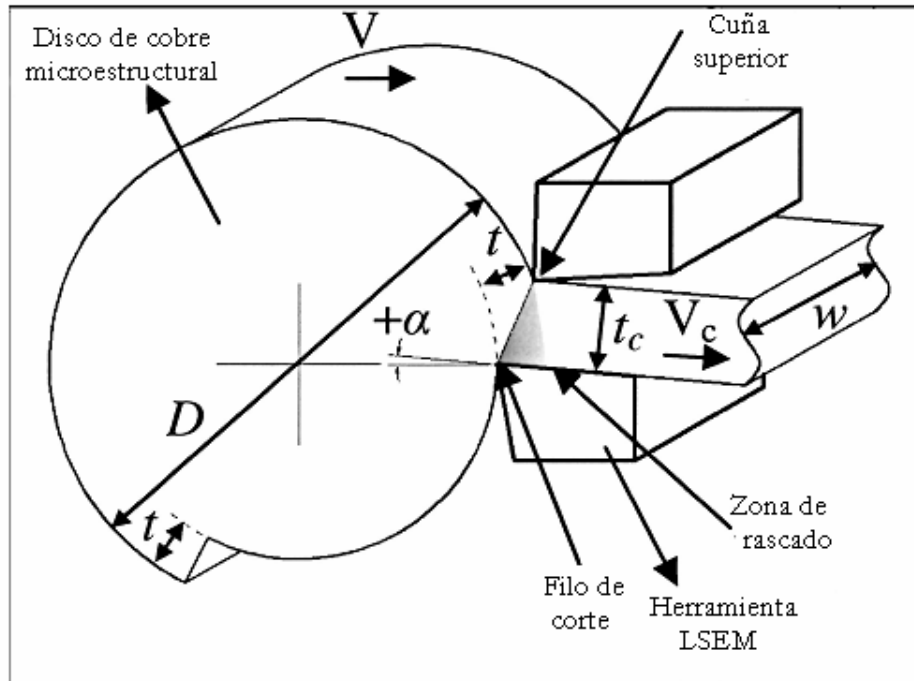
Herramienta de mecanizado con extrusión bajo alta deformación.
